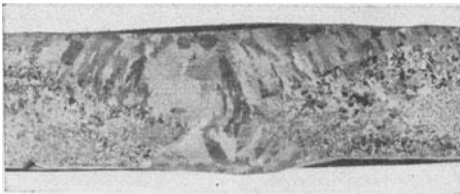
Querschnitt einer Kohlebogen-Kupfer-Schweißnaht (Schliffbild).
